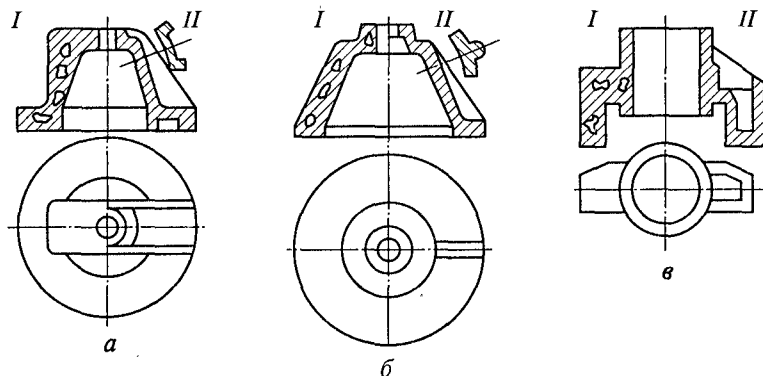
Варианты (*a*—*в*) конструкций отливок:
